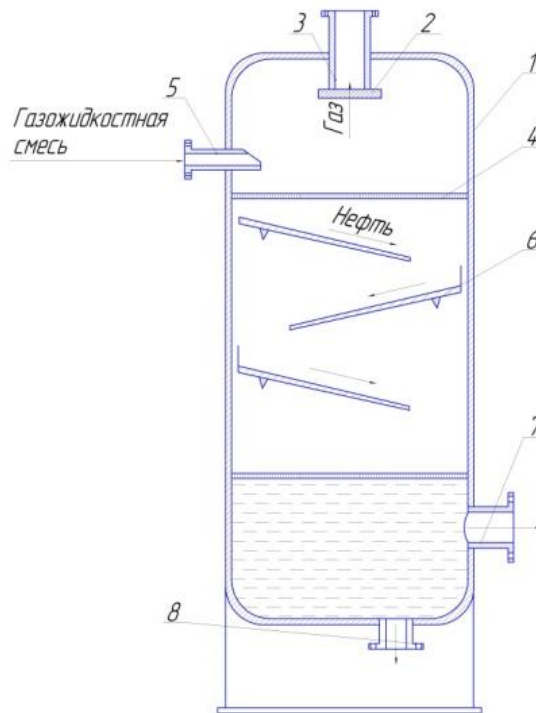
Вертикальный нефтегазовый сепаратор: 1 – корпус; 2 – каплеотбойник; 3 – выход газа; 4 – стабилизатор потока; 5 – вход смеси; 6 – наклонный лоток; 7 – сброс нефти; 8 – сброс грязи
